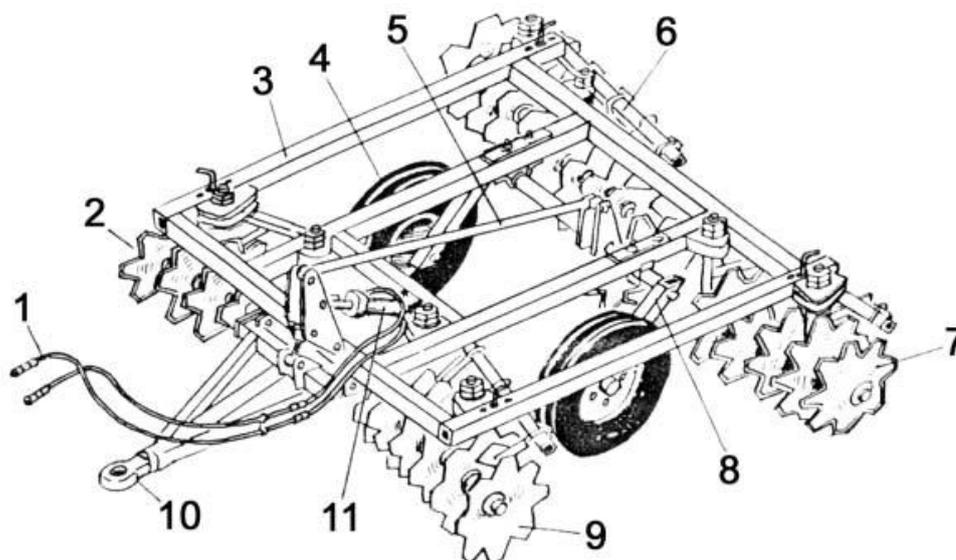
Общий вид бороны дисковой тяжелой Л-113-02
